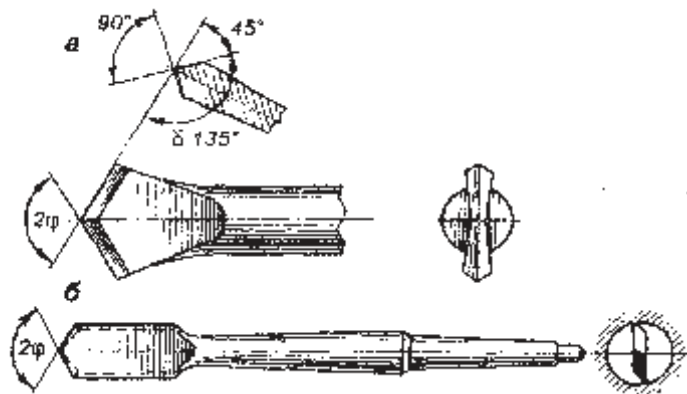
Сверла, оснащенные пластинками из твердого сплава
